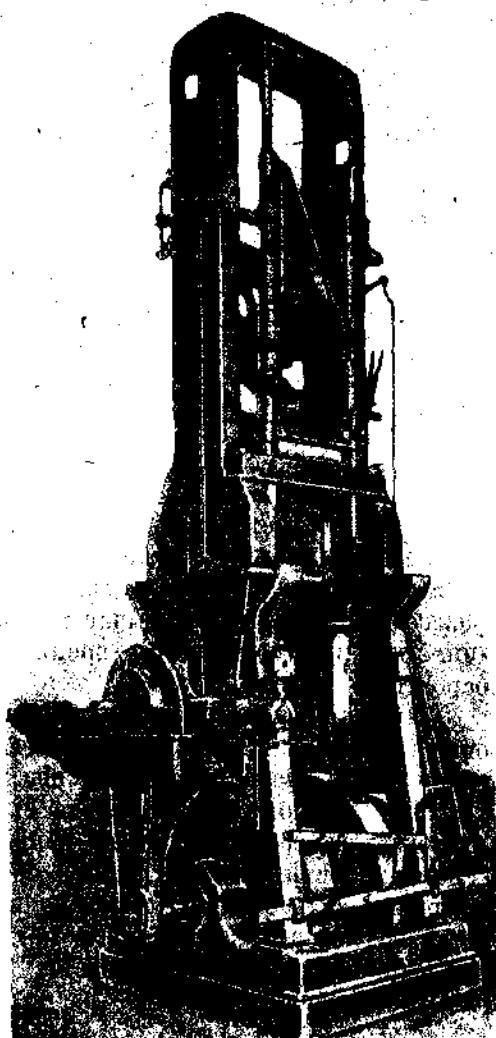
Автоматический лесопильный станок Болиндера, патент инж. Тенова.
